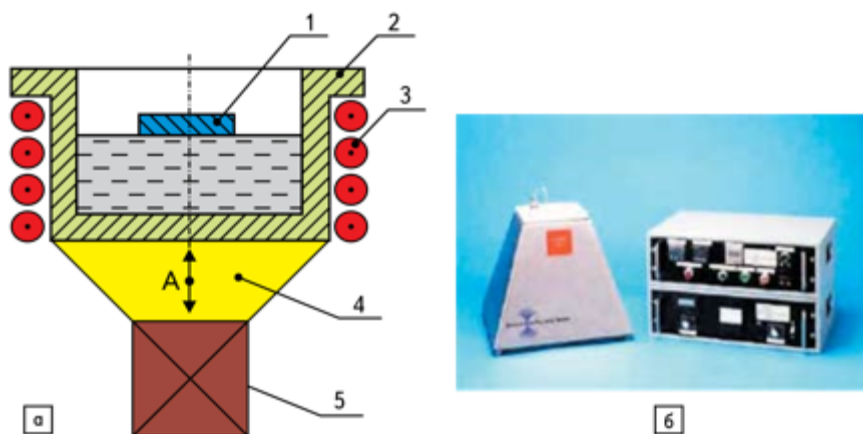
УЗ-ванна с возбуждением всей массы припоя: а – схема: 1 – паяемая деталь; 2 – ванна; 3 – нагреватель; 4 – излучатель; 5 – реобразователь; б) общий вид
